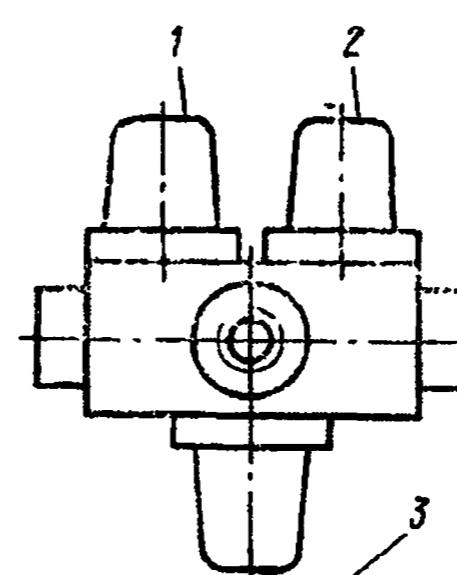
Расположение регулировочных винтов тройного защитного клапана:
